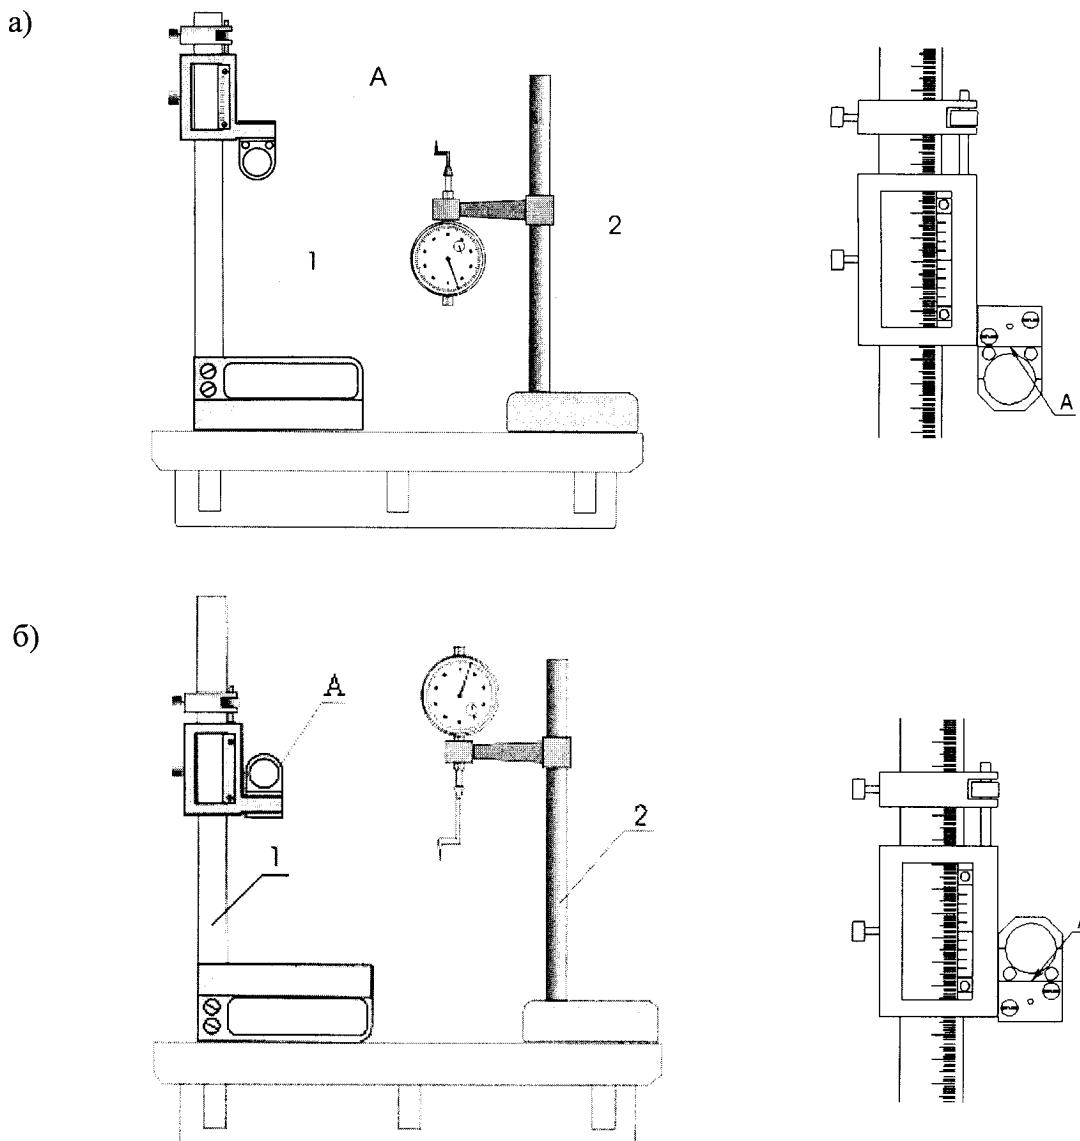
Определение отклонения от параллельности расположения базовой опорной поверхности (А) под шпонку целевого знака относительно базовой поверхности основания корпуса
